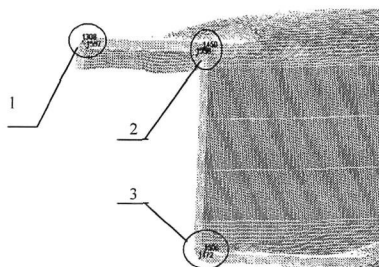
Общий вид 1/2 полной модели заготовки с зонами сгиба
